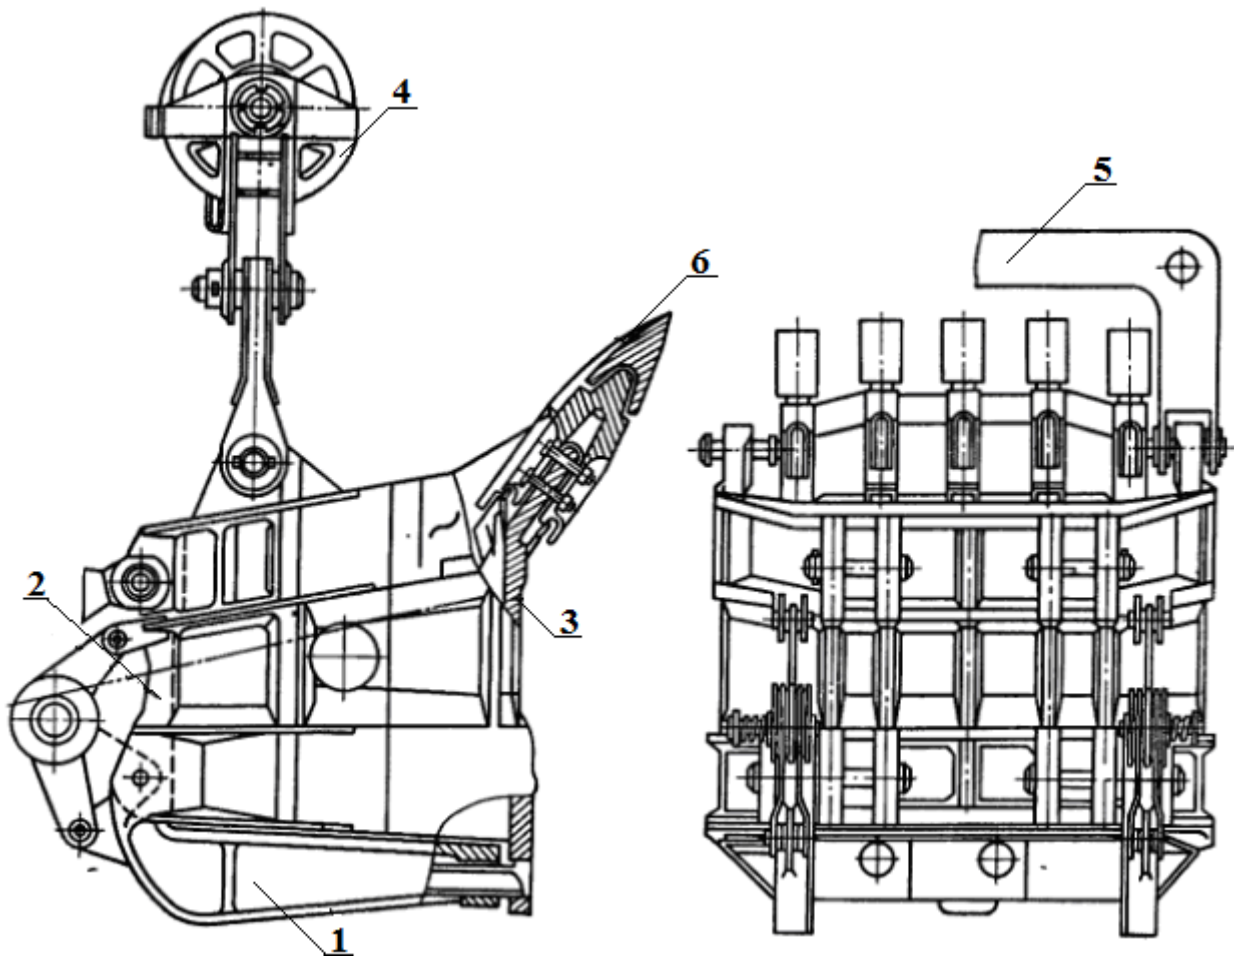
Конструктивна схема зварно-литого ковша екскаватора ЕКГ-12,5
